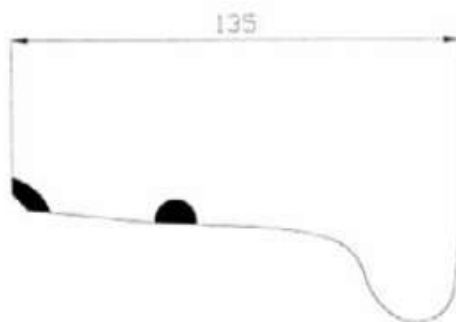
Zona de localización de fisuras térmicas en la llanta (medidas en mm).
